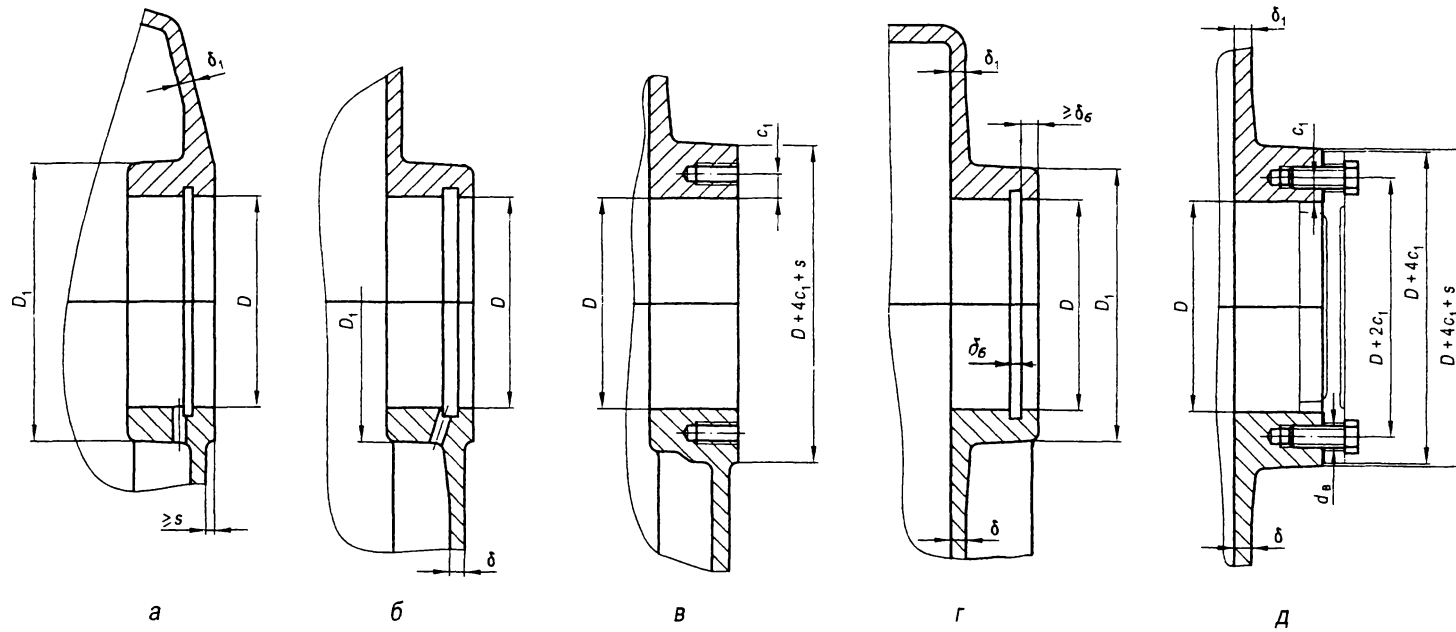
Приливы (бобышки) для подшипников (размеры см. в табл. 11.2.1 и 11.5.1) [1]
